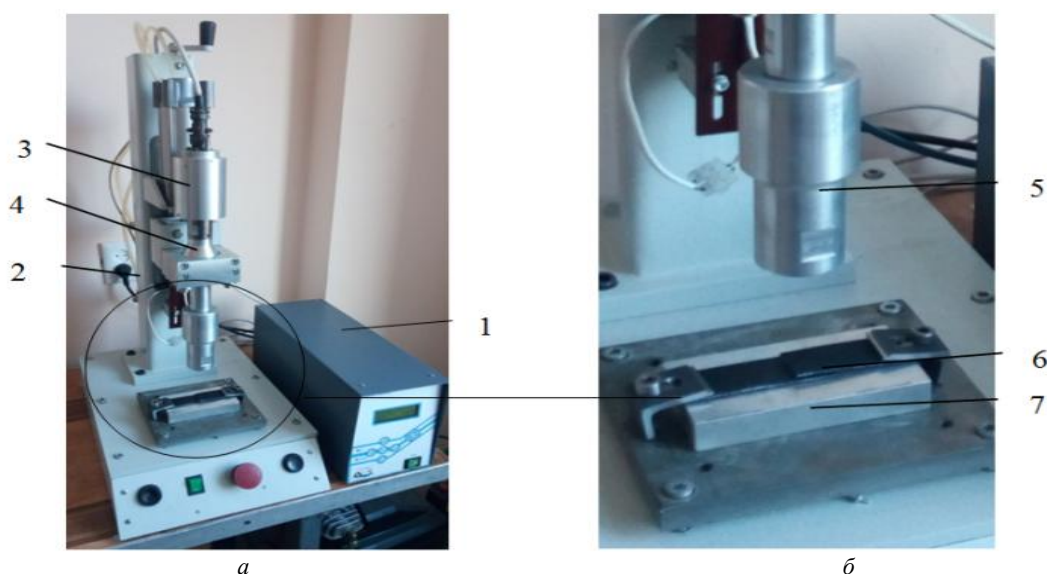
Ультразвуковая сварочная машина: *а* — общий вид; *б* — зона ультразвуковой сварки; 1 — ультразвуковой генератор, 2 — пневматический пресс, 3 — пьезоэлектрический преобразователь, 4 — бустер, 5 — волновод-излучатель, 6 — свариваемые детали, 7 — ложемент.
